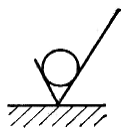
Знак, применяемый для обозначения шероховатости на чертеже
